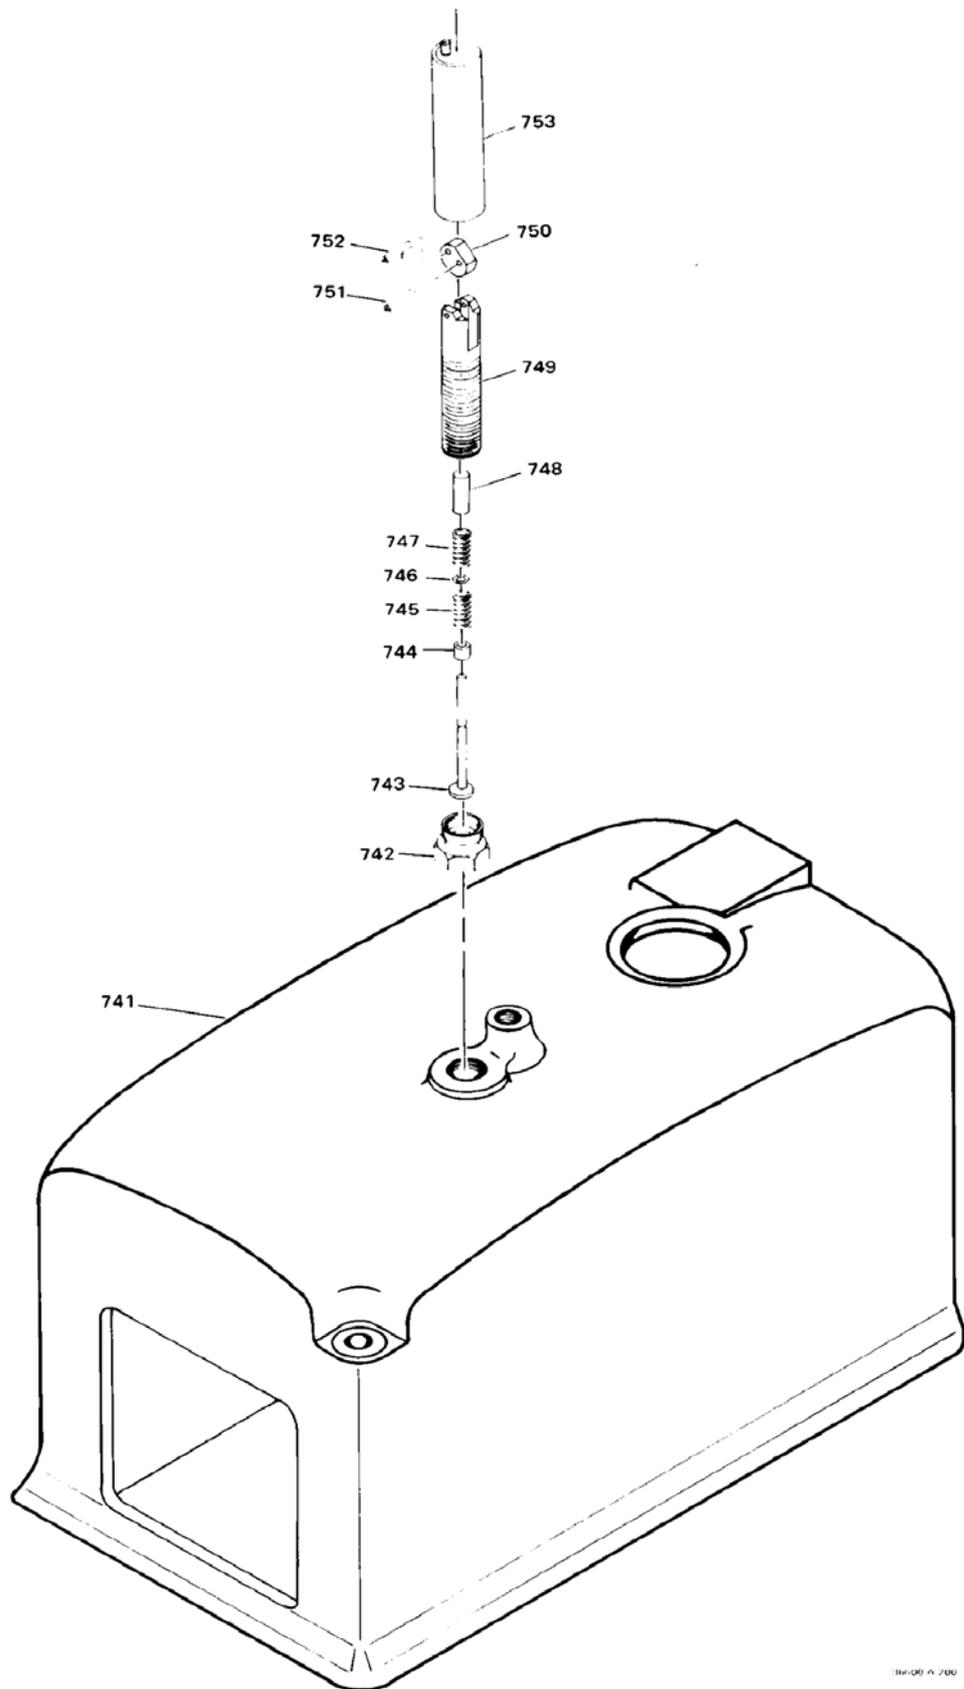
Покомпонентный чертеж устройства проверки регулятора предельных оборотов
